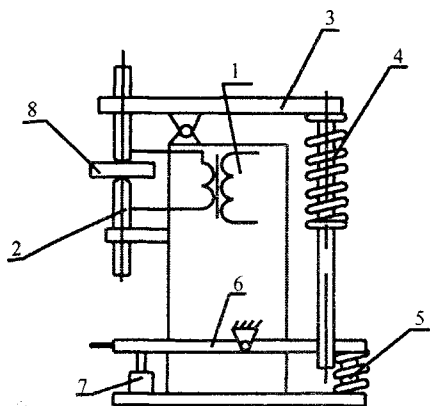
Конструктивная схема машины для точечной сварки: 1 – сварочный трансформатор; 2 – электроды; 3...6 – рычажный механизм сжатия; 7 – электропневматический привод сжатия электродов; 8 – свариваемое изделие
